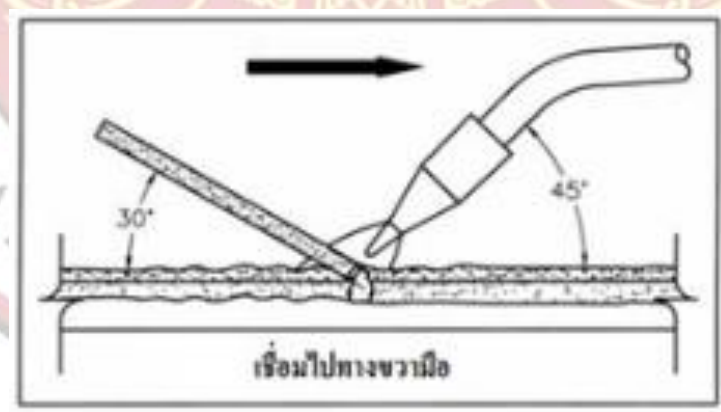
การเชื่อมต่อชนบากงาน (Beveled Butt Welding)
